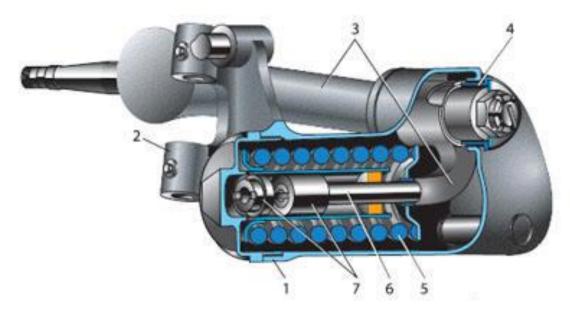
Независимая подвеска «Дюбоне»: 1 — корпус; 2 — ушки шкворня; 3 — рычаг; 4 — игольчатый подшипник; 5 — пружина; 6 — шток поршня; 7 — клапаны
